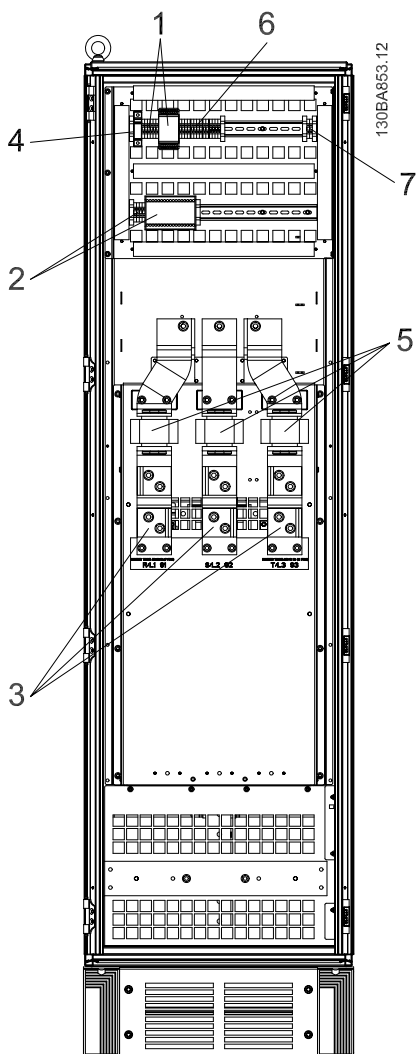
Дополнительный шкаф, размер корпуса F3 и F4
